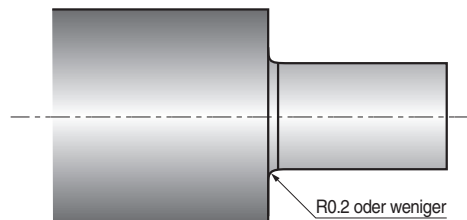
Beispiel für einen festgelegten Eckradius in der Zeichnung
